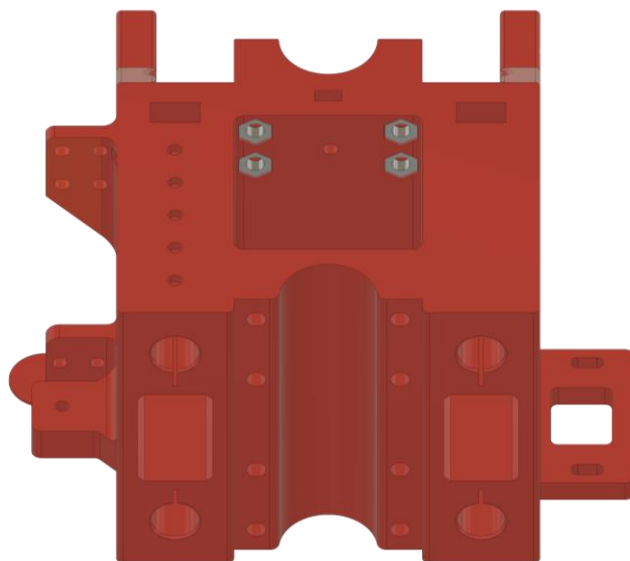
Komponenty pro sestavení osy X - část s krokovými motory
